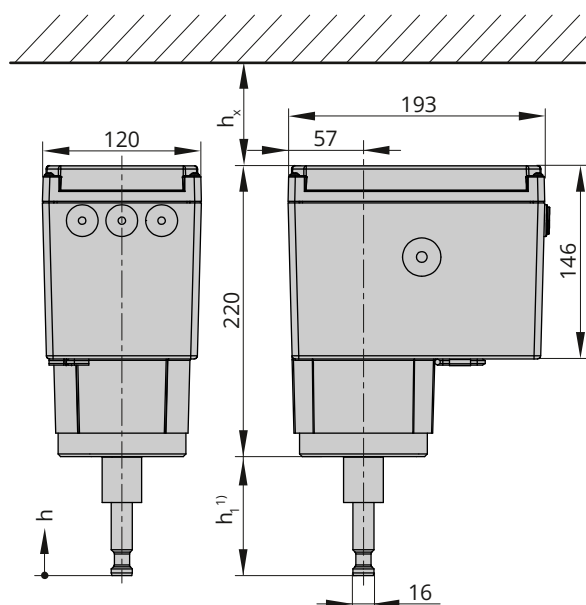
Dimensions en mm · Types 3374-15, -17, -26 et -36, (Forme A)
